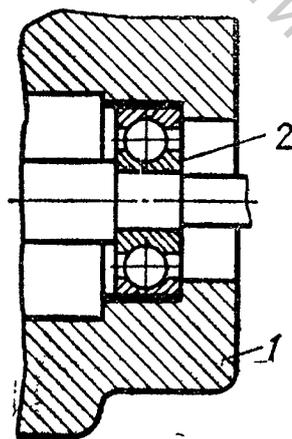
Посадка подшипника качения в корпус оборудования
